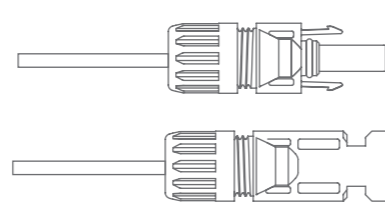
Stecker mit aufgeschraubter Überwurfmutter
